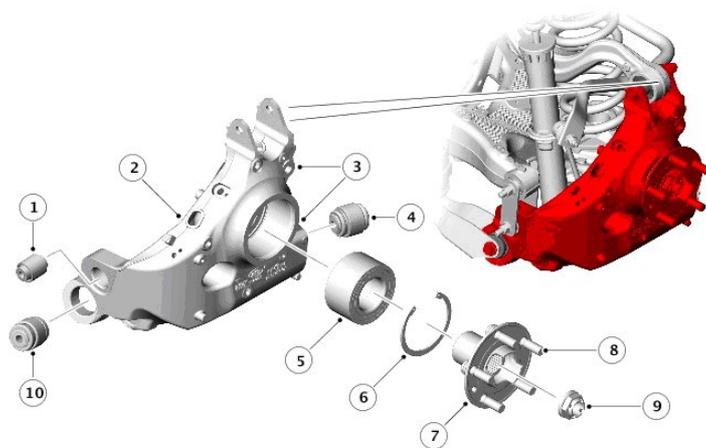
Цапфа и ступица колеса с подшипником задней подвески Discovery Sport в сборе
